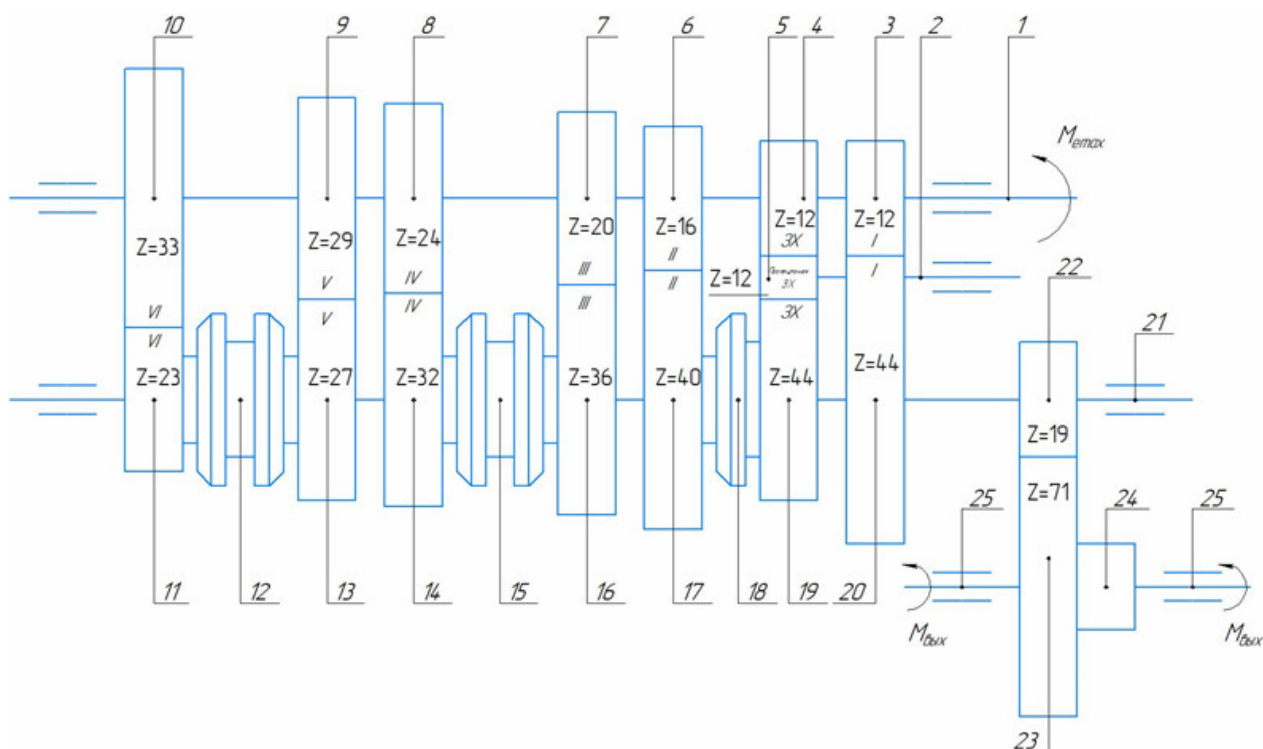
Кинематическая схема шестиступенчатой МКПП
